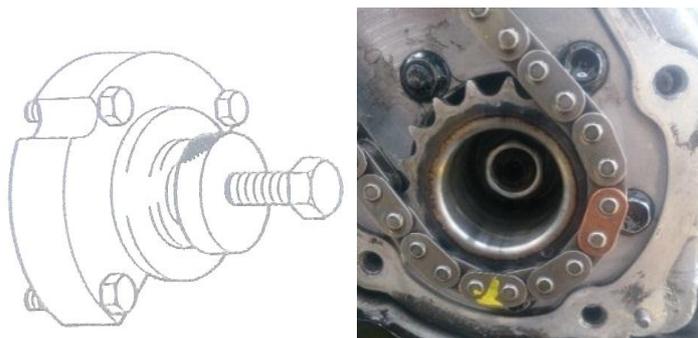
Rueda dentada de la bomba de alta presión y extractor de tuerca.
